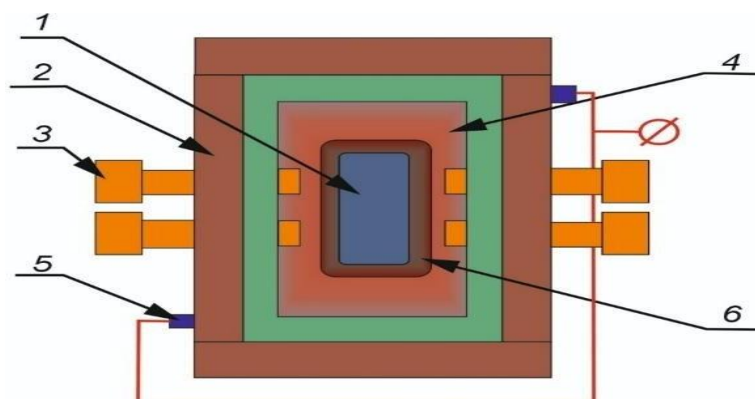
Схема процесу електрошлакового наплавлення плоских заготовок у струмопідвідному кристалізаторі з квадратною формуючою секцією [68]: 1 – заготовка, що наплавляється; 2 – панель струмопідвідної секції кристалізатора; 3 – дозатор; 4 – шлакова ванна; 5 – струмопідведення; 6 – наплавлений метал
